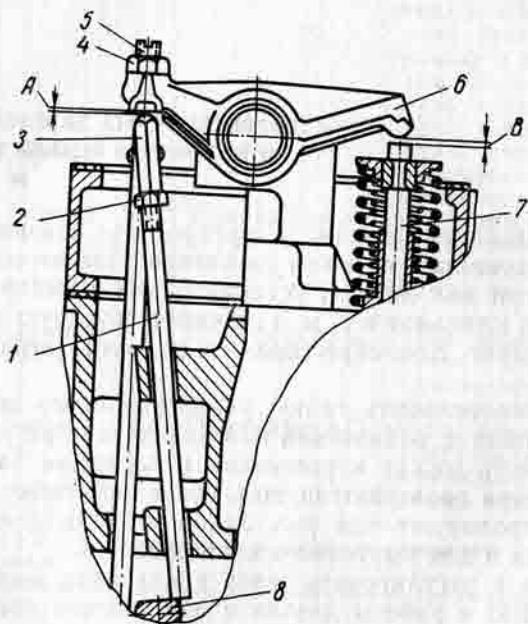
Регулировка зазоров клапанов и механизма декомпрессора:
